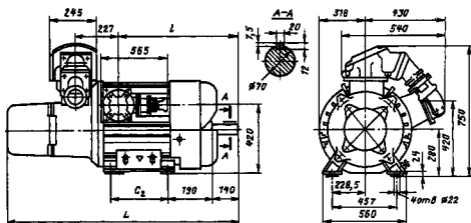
25 Габаритные и установочно-присоединительные размеры и масса двигателей ВАОК 9 Размеры, мм, и масса приведены в таблице
